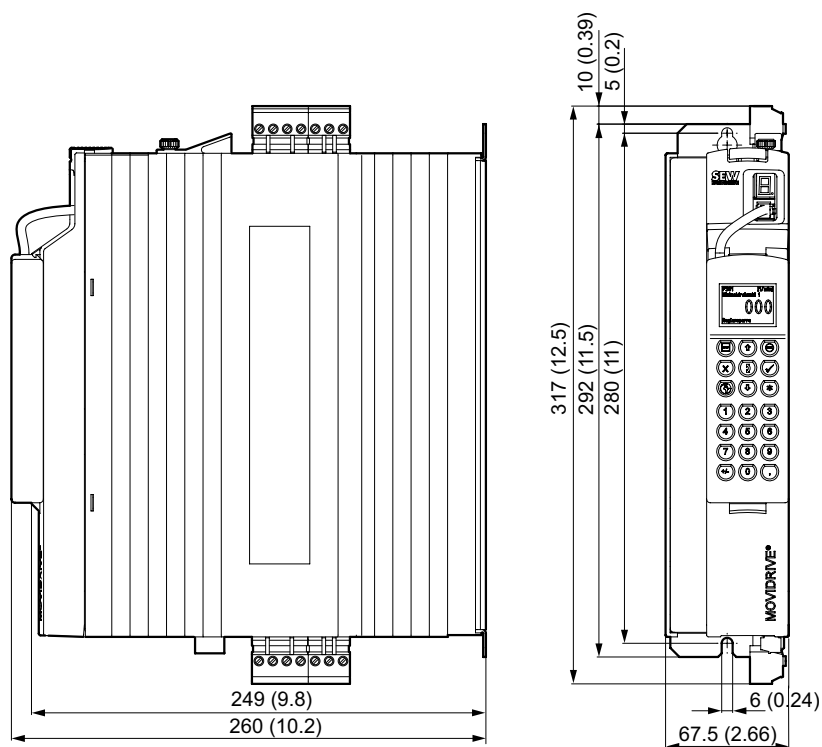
Dimensionais MDX60B, tamanho 0M, dimensões em mm (in)
